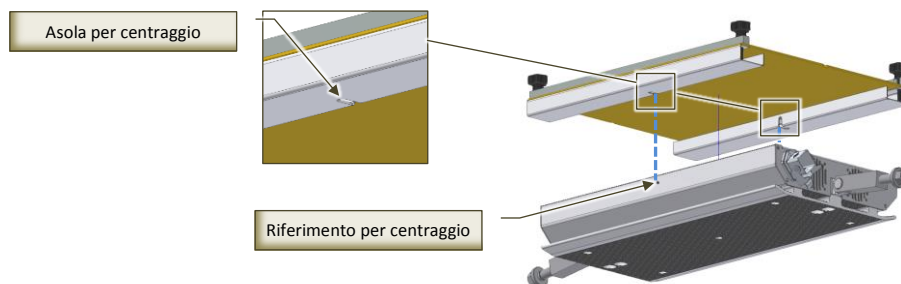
Posizionamento piastra di giunzione su piastra inferiore pressa
